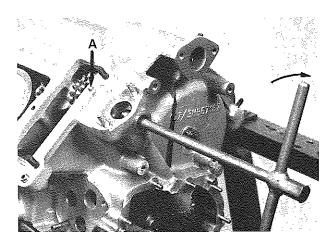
Estrattore n. 12 - A) Vite Puller No. 12 - A) Screw
